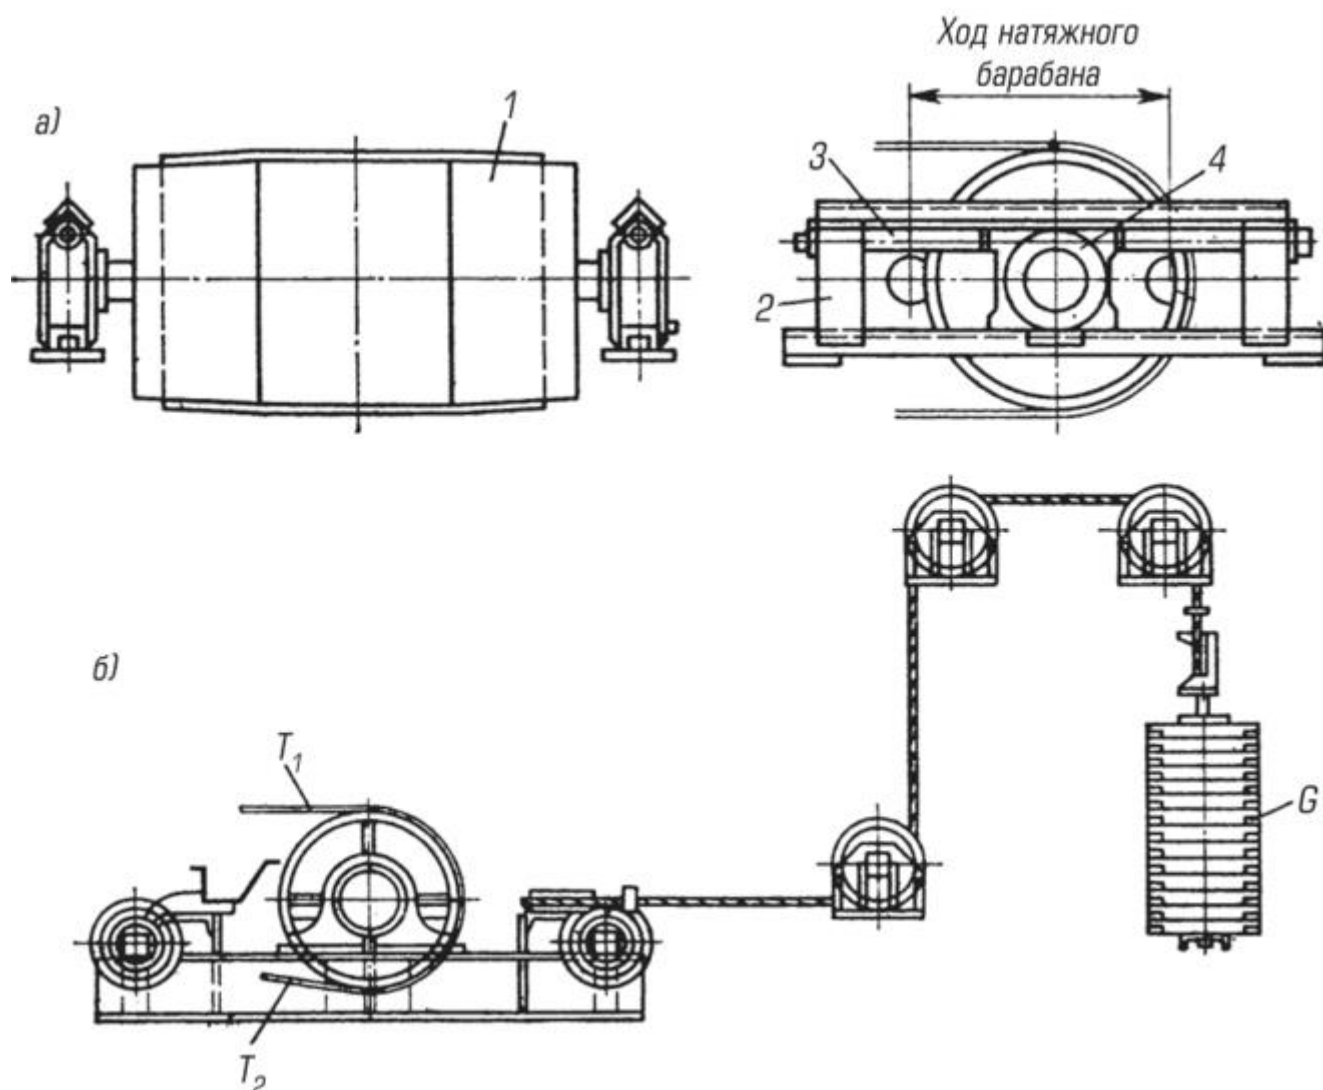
Схемы натяжных устройств натяжения ленты при ее вытягивании. Натяжной барабан устройства (рис. 2.9, б) укрепляют, как и барабан винтового устройства, в корпусах, передвигающихся по направляющим, или на специальной тележке. Тележка соединяется канатом или цепью с грузом С, создающим неизменные значения натяжения T_1 и T_2 ветвей ленты.
